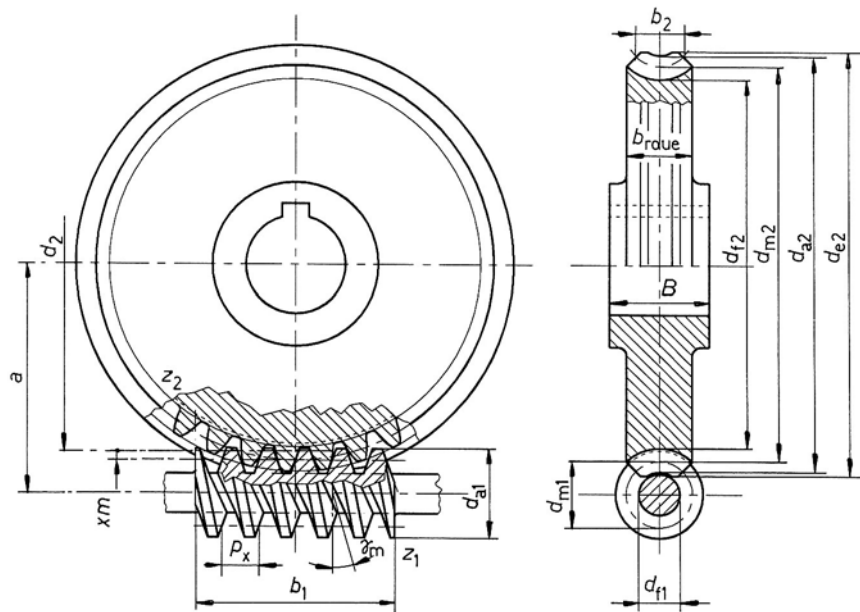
Dimensions générales de l'engrenage à vis sans fin
